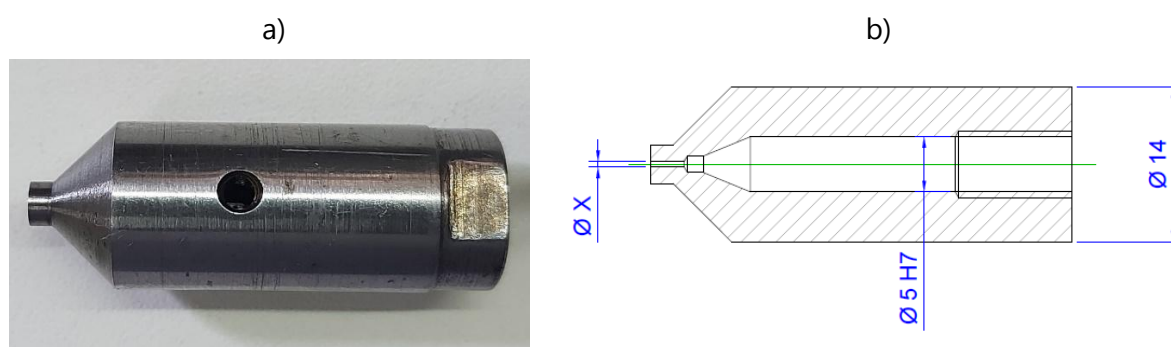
Corpo da ferramenta: a) ferramenta, b) desenho esquemático para ferramentas de 0,5 mm a 1,0 mm
